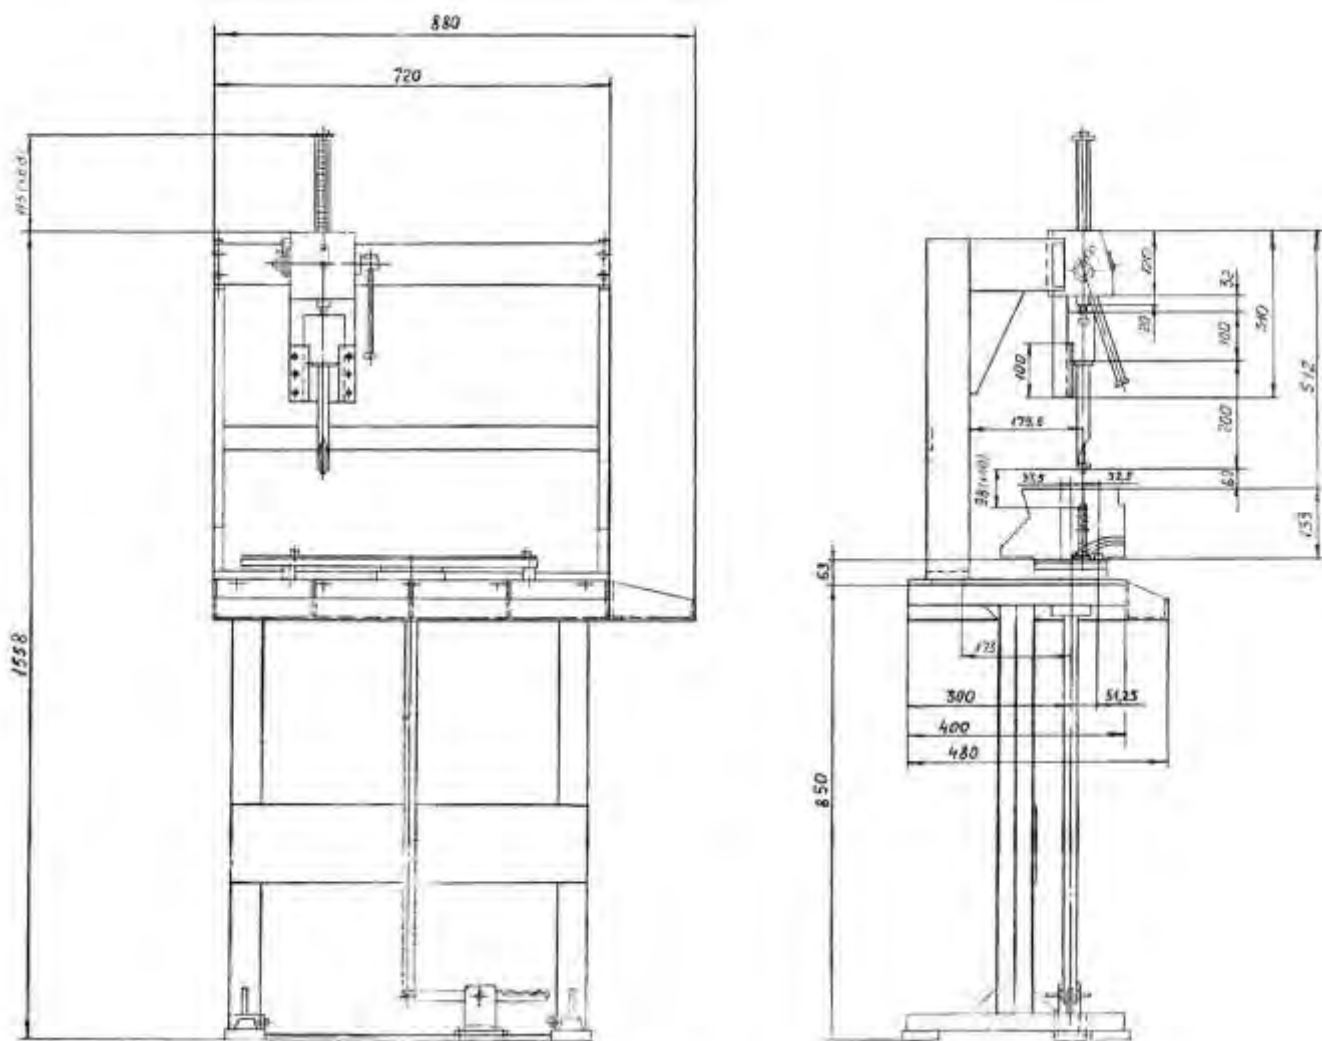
3М 7823-4629 Приспособление для засухаривания
